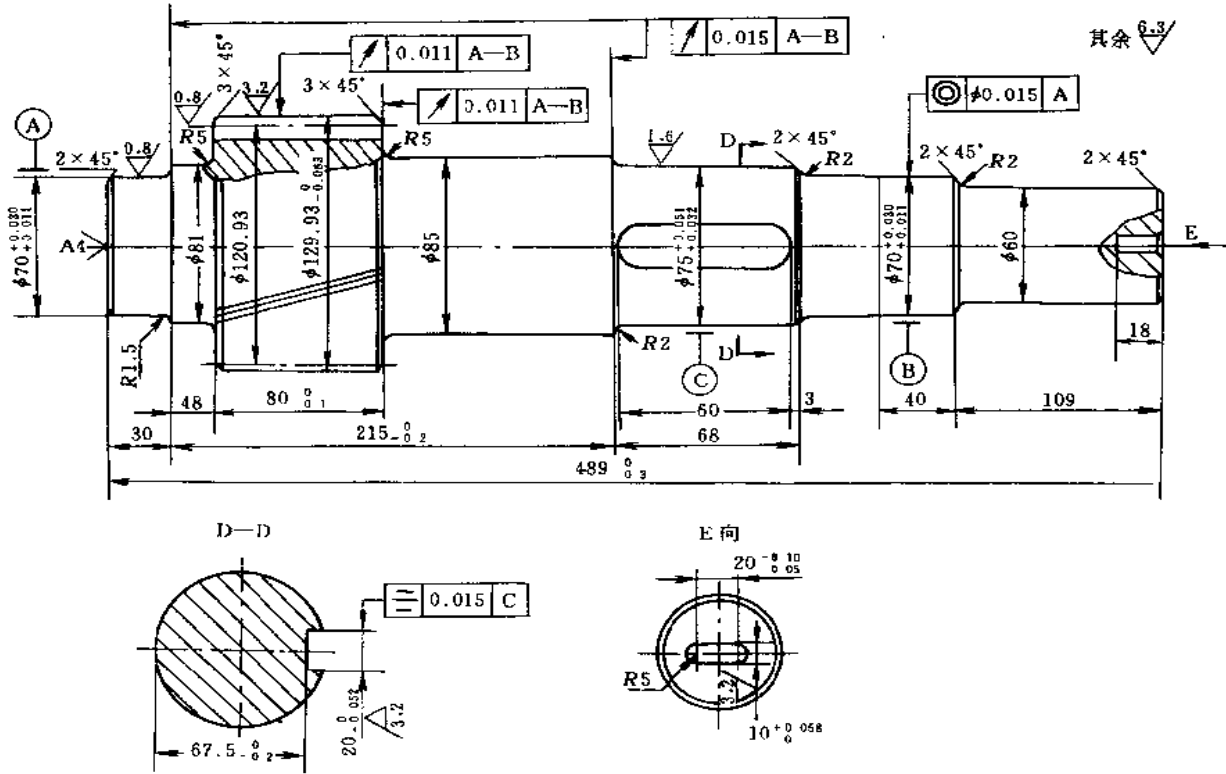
齿轮轴 (材料: 42CrMoA)
